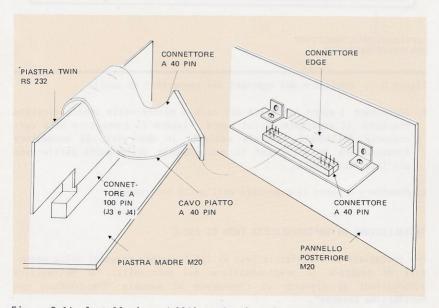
Installazione dell'interfaccia twin RS 232-C
